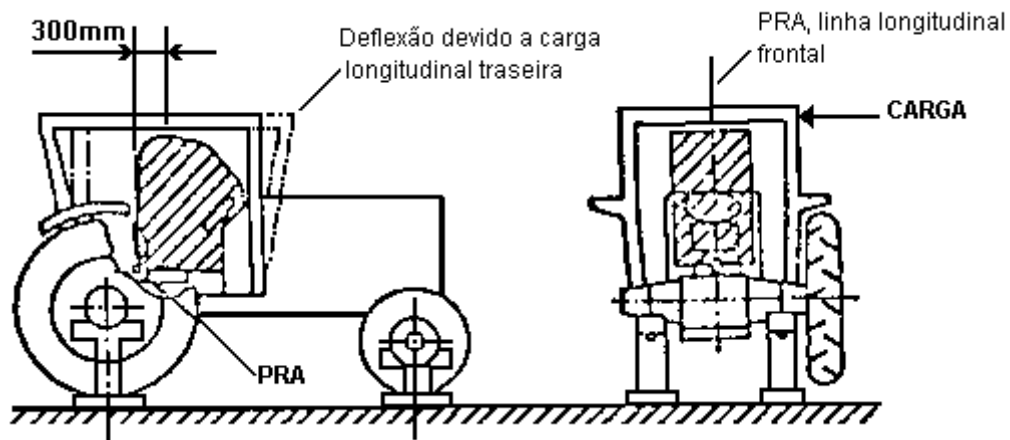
Ponto de aplicação da carga no ensaio de carregamento lateral.
